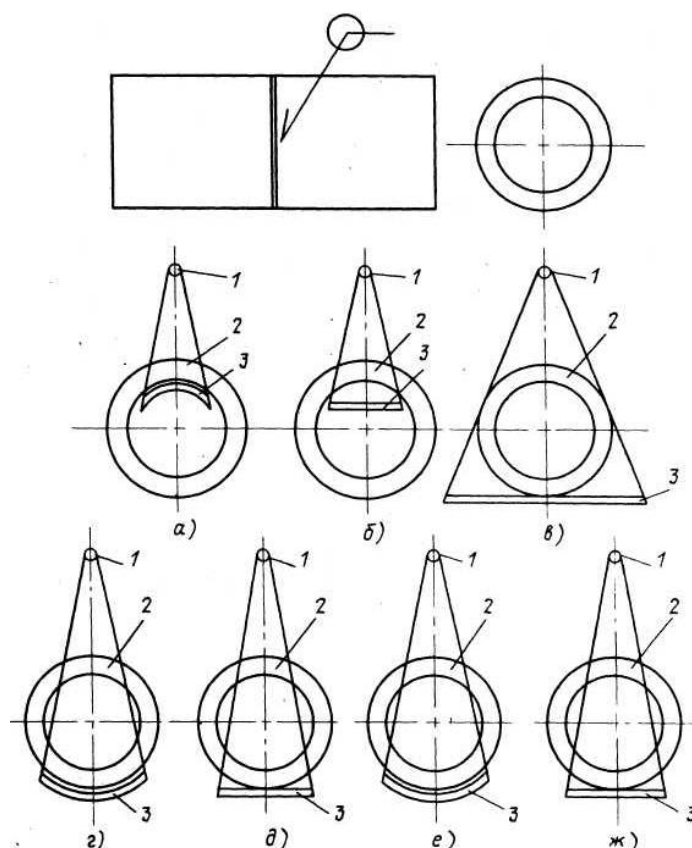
Схемы контроля кольцевых сварных соединений:
